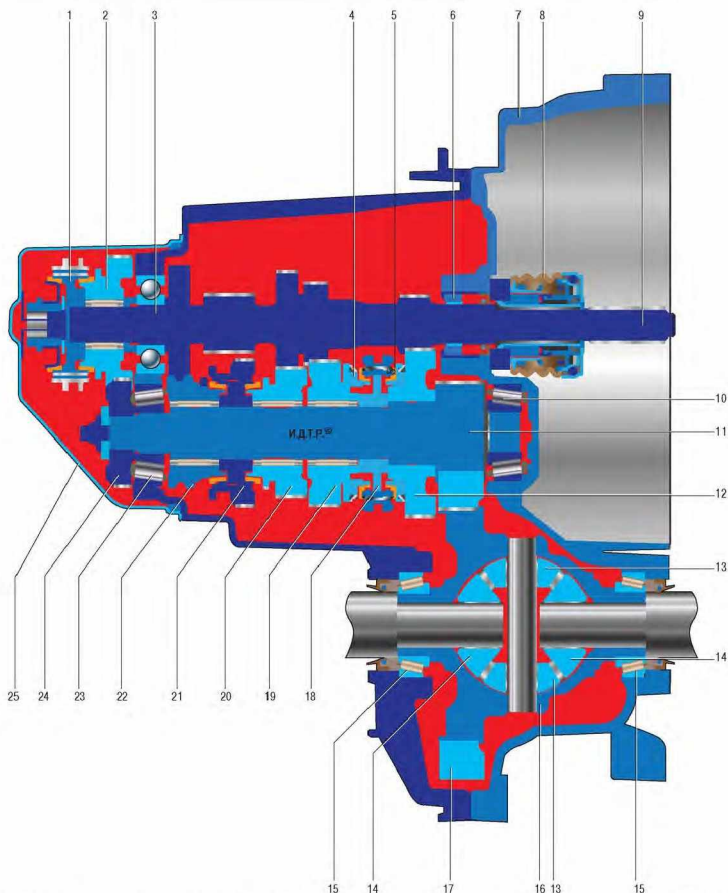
Схема 5-ступенчатой механической коробки передач модели RS5F92R: 1 – синхронизатор V и передачи заднего хода; 2 – ведущая шестерня V передачи; 3 – задний подшипник первичного вала; 4 – конический синхронизатор II передачи; 5 – конический синхронизатор I передачи; 6 – передний подшипник первичного вала; 7 – кожух сцепления; 8 – рабочий цилиндр выключения сцепления; 9 – первичный вал; 10 – передний подшипник вторичного вала; 11 – вторичный вал; 12 – ведомая шестерня I передачи; 13 – сателлит; 14 – шестерня дифференциала; 15 – подшипник дифференциала; 16 – коробка дифференциала; 17 – шестерня главной передачи; 18 – синхронизатор I и II передач (сборка); 19 – ведомая шестерня второй передачи; 20 – ведомая шестерня III передачи; 21 – синхронизатор III и IV передач; 22 – ведомая шестерня IV передачи; 23 – задний подшипник вторичного вала; 24 – ведомая шестерня V передачи; 25 – крышка картера коробки передач
